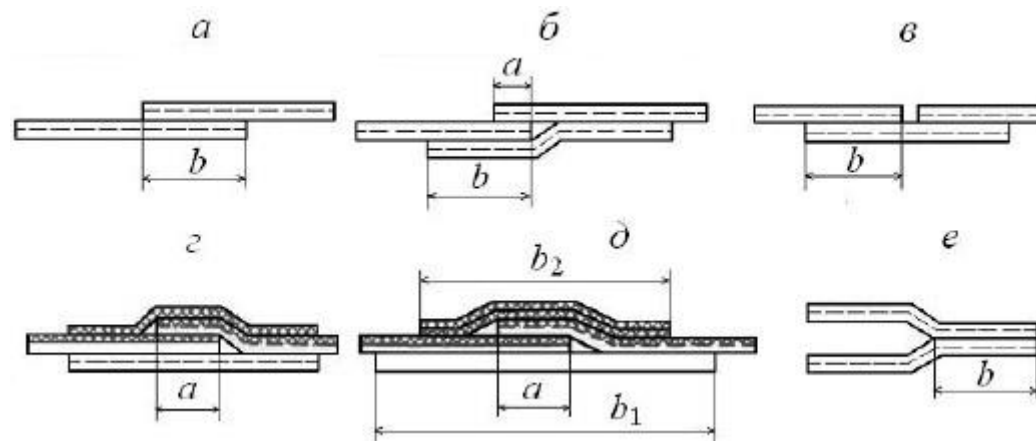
Виды сварных соединений пленок: а – однослойные внахлестку; б - однослойные внахлестку с накладкой; в - однослойные встык с накладкой; г – армированные внахлестку с накладками из основной и армирующей пленок; д – армированные внахлестку с накладками из основной и двух слоев армирующей пленки; е – Т-образное с рантовым швом
